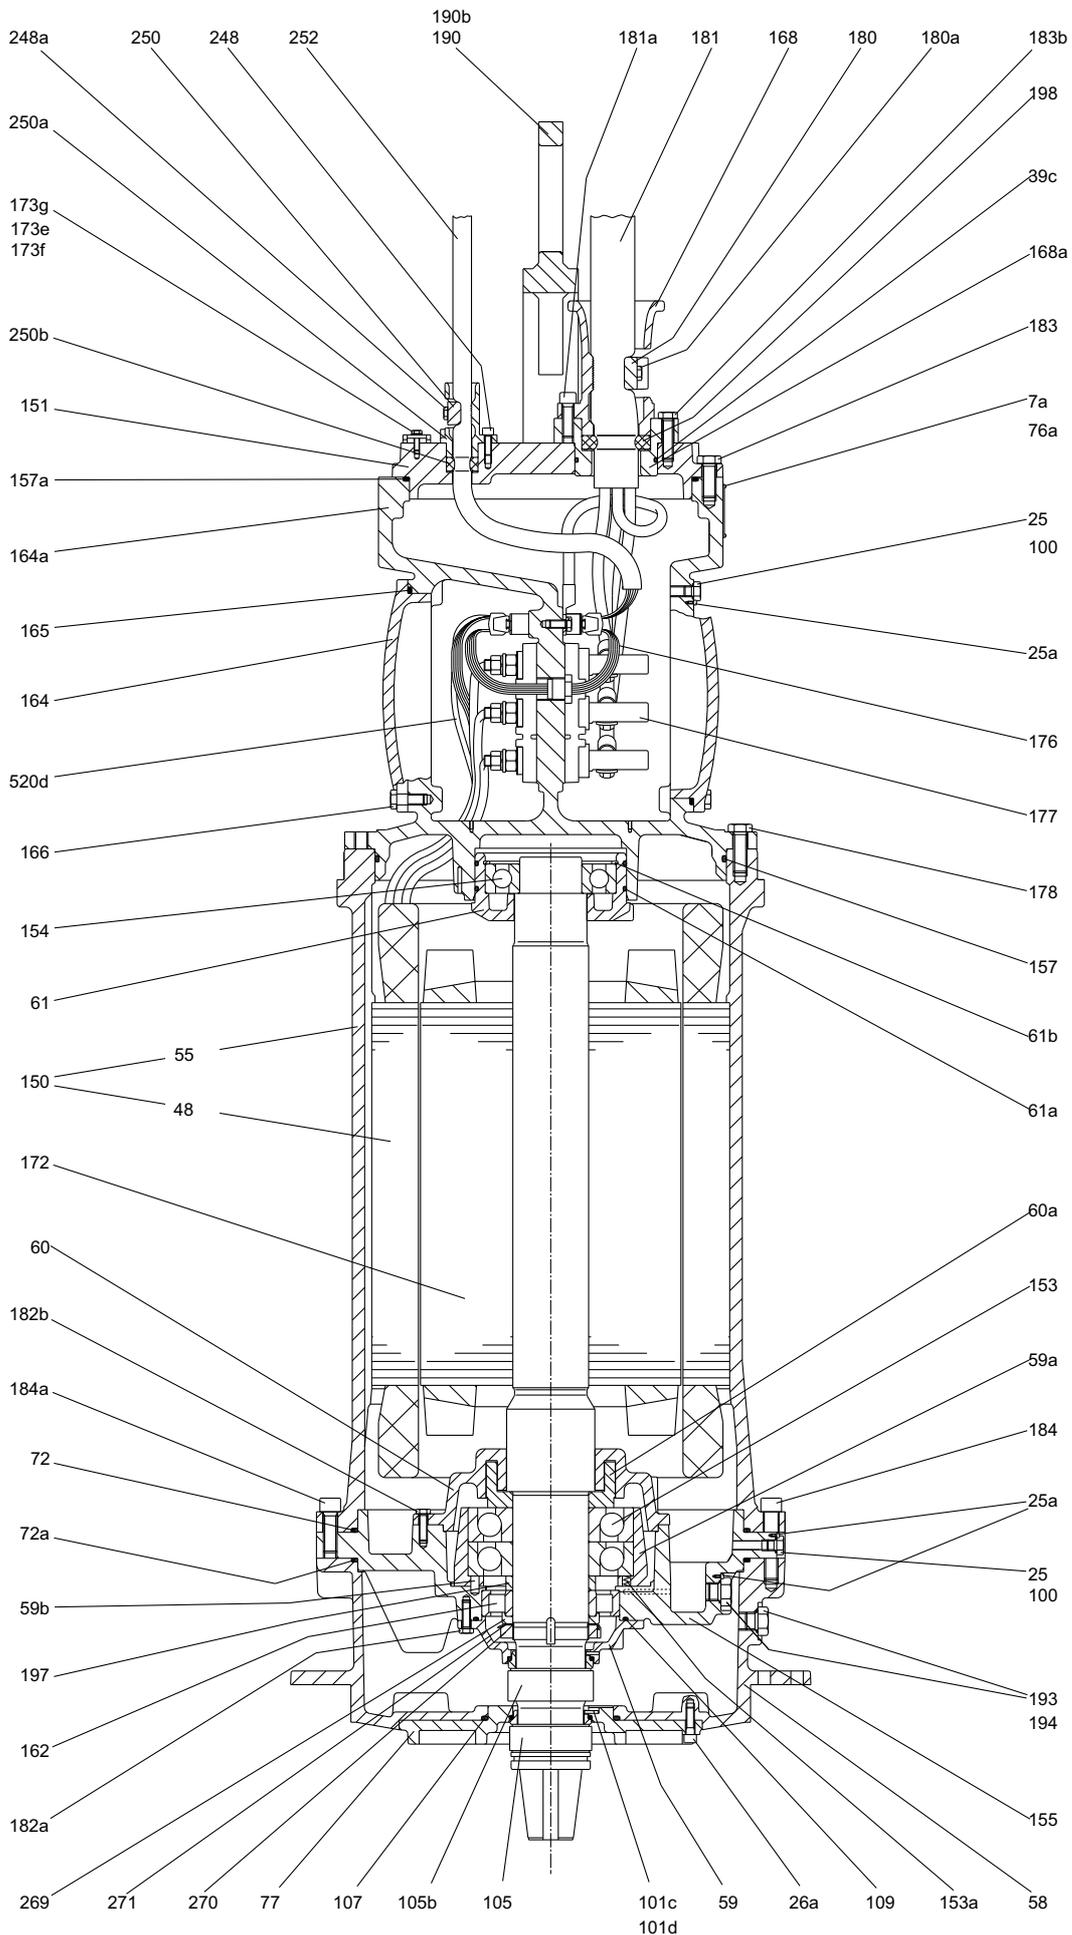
Взрывозащищённый электродвигатель, установка в обсадной трубе (ST)
